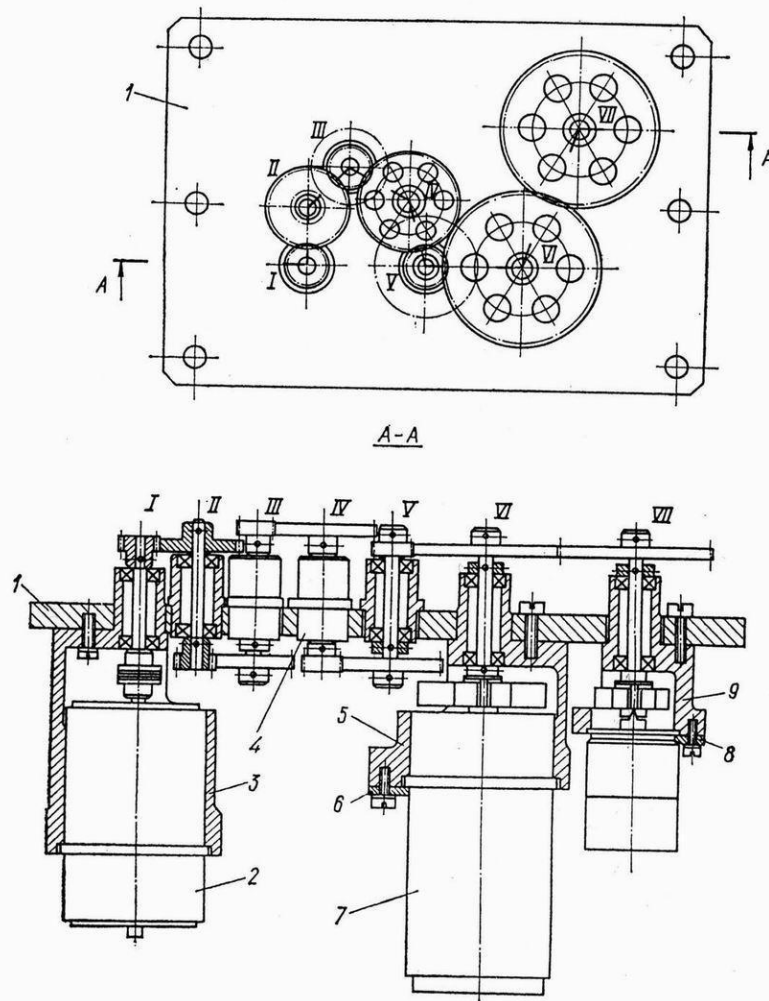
Конструкція одноплатного зубчастого редуктора системи управління
